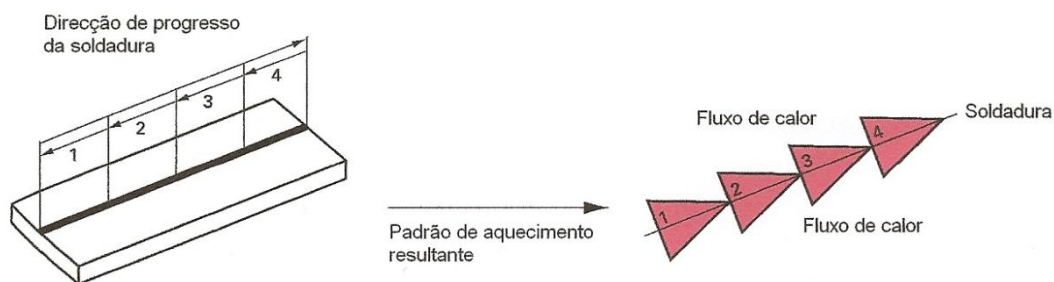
Sequência de soldadura com “passo de peregrino”
